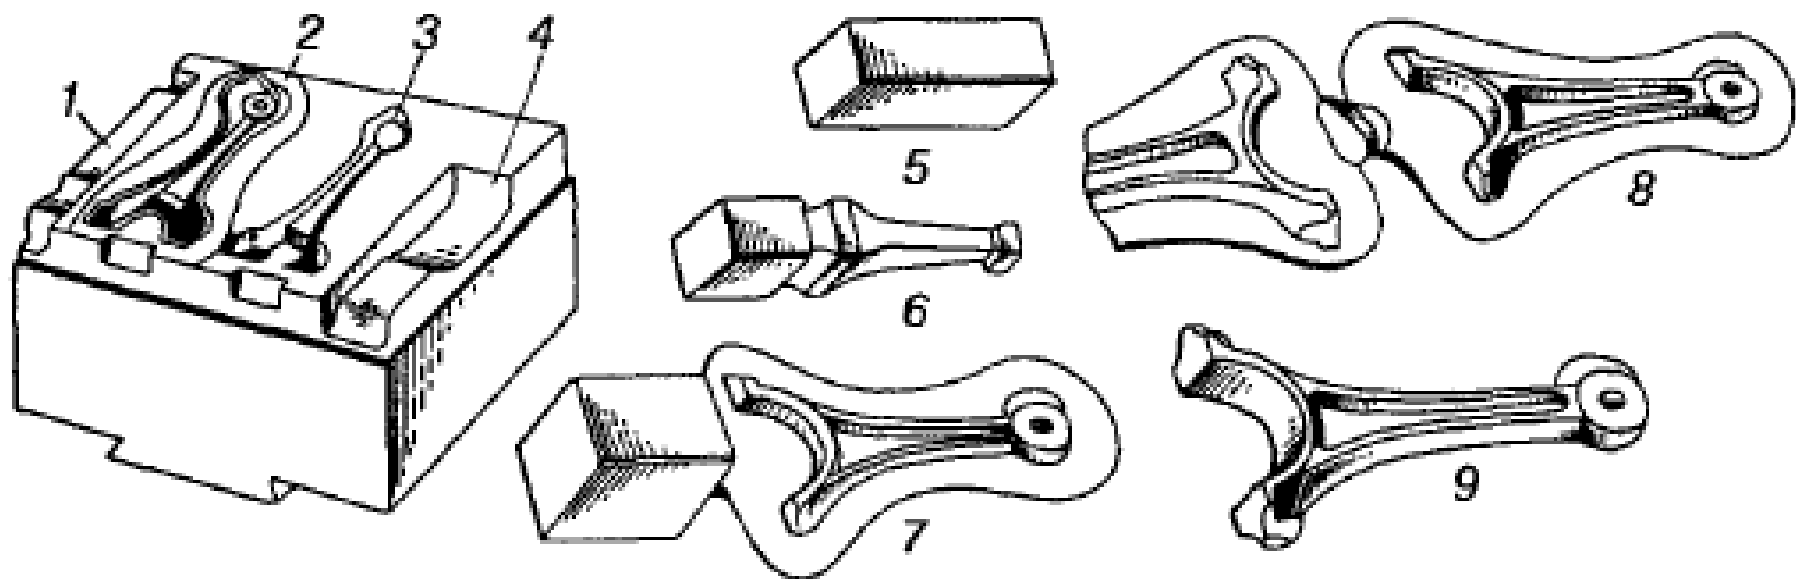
Штампування шатуна в багаторівчачковому молотовому штампі
